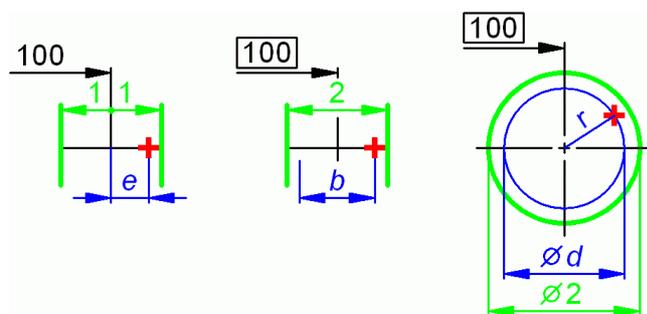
Toleranzen und Abweichungen: Links Abstand, mitte Position in einer Richtung, rechts Position in beliebiger Richtung mit kreisförmiger Toleranzzone
